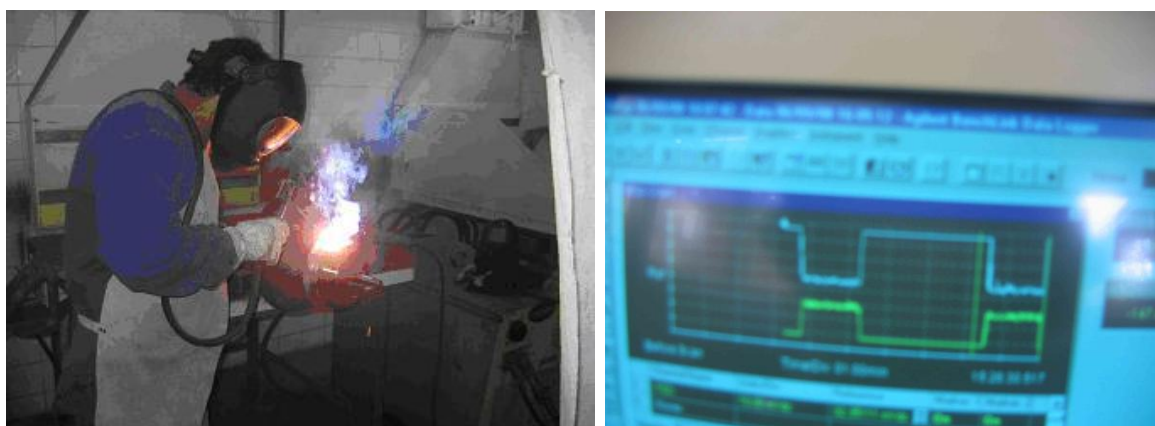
Soldagem do bocal e detalhe do sistema de aquisição de dados.
